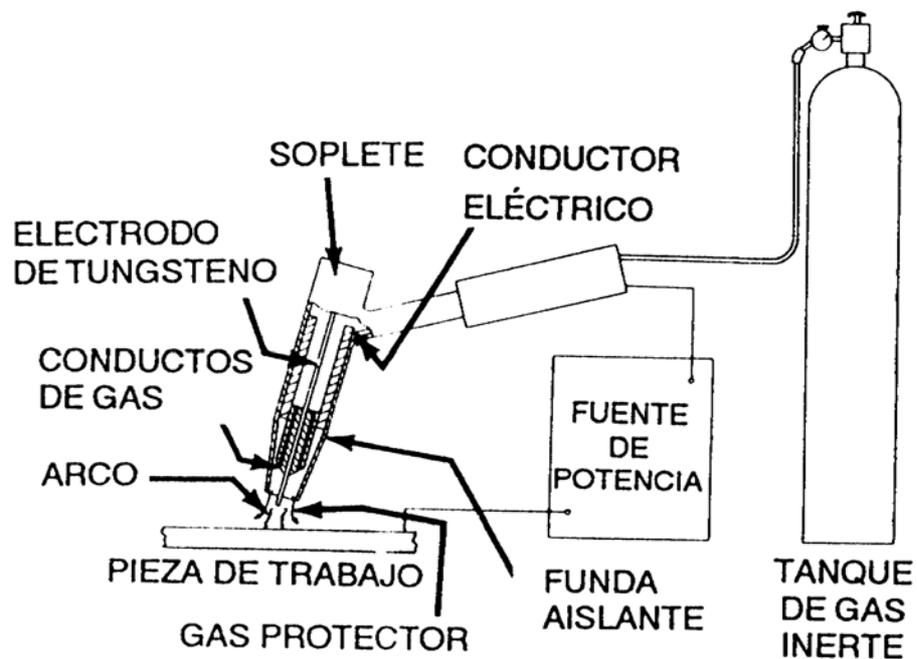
Disposición del equipo para soldadura por arco de tungsteno y gas
